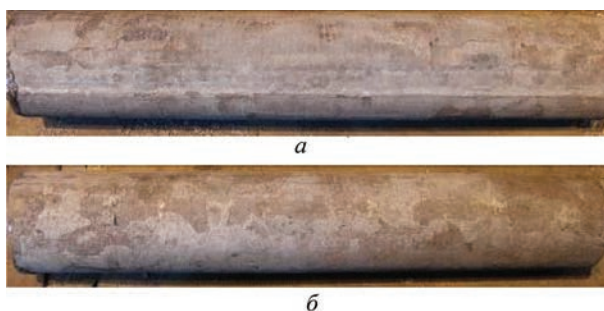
Внешний вид непрерывнолитых заготовок диаметром 200 мм, выданных на возврат после нагрева в кольцевой печи: а – сталь марки 32Г2; б – сталь марки 20
